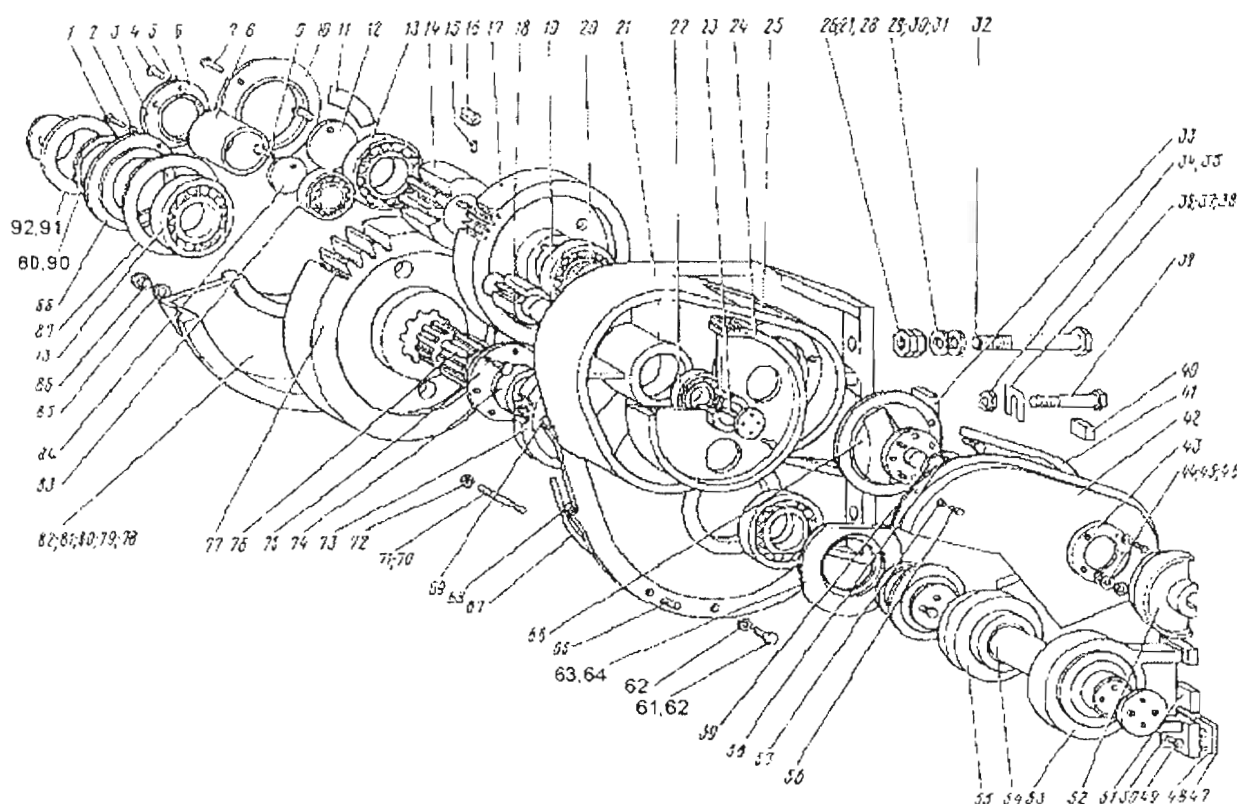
Схема сборки/разборки редуктора хода ЭКГ-5А
